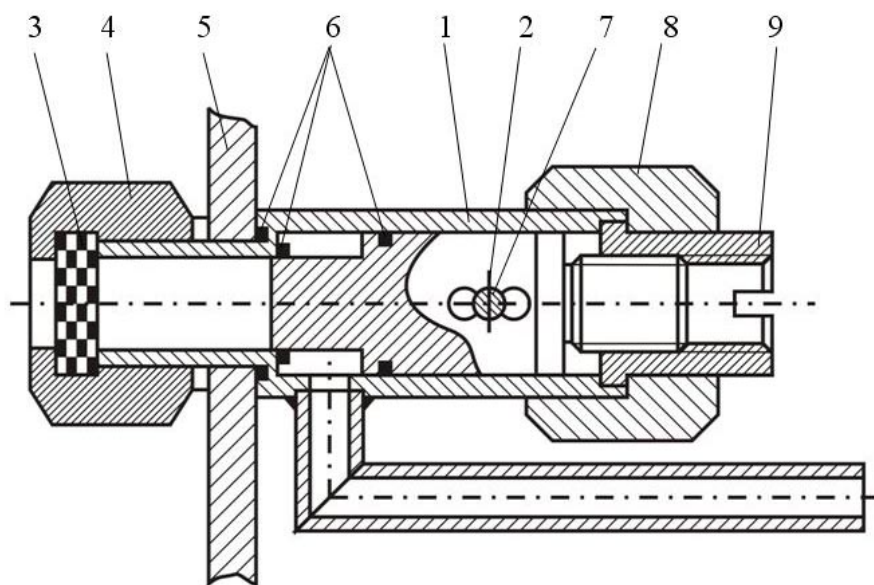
Клапан: 1 – корпус; 2 – клапан; 3 – пылевой фильтр; 4 – колпачковая гайка; 5 – крышка барабана шаровой мельницы; 6 – уплотнительные кольца; 7 – штифт цилиндрический; 8 – гайка колпачковая; 9 – резьбовая втулка
